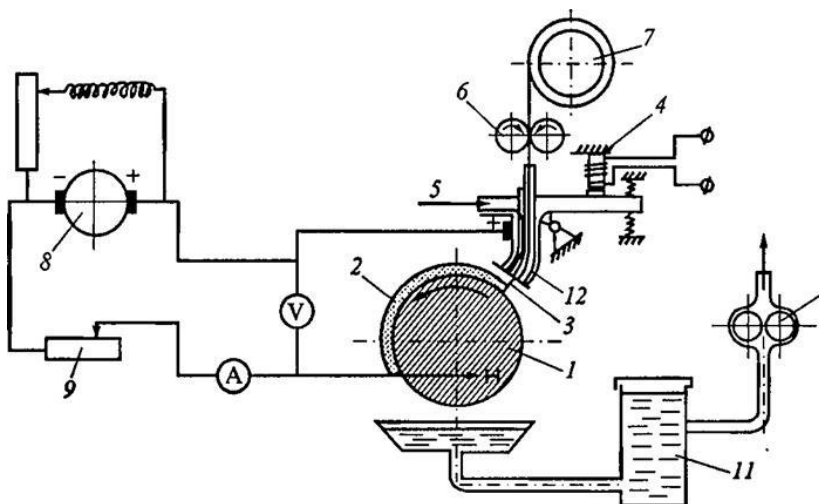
Схема вибродуговой установки для наплавки деталей:
